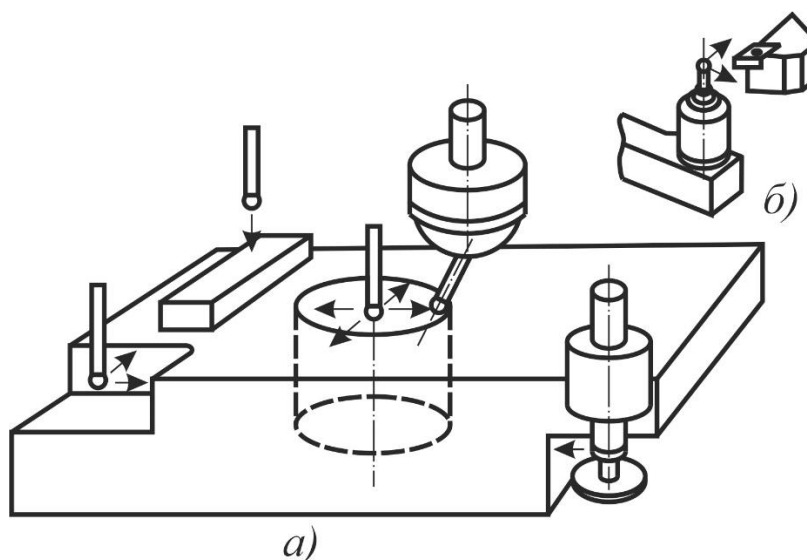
Схема измерений обрабатываемой детали (а) и режущего инструмента (б) щупами
